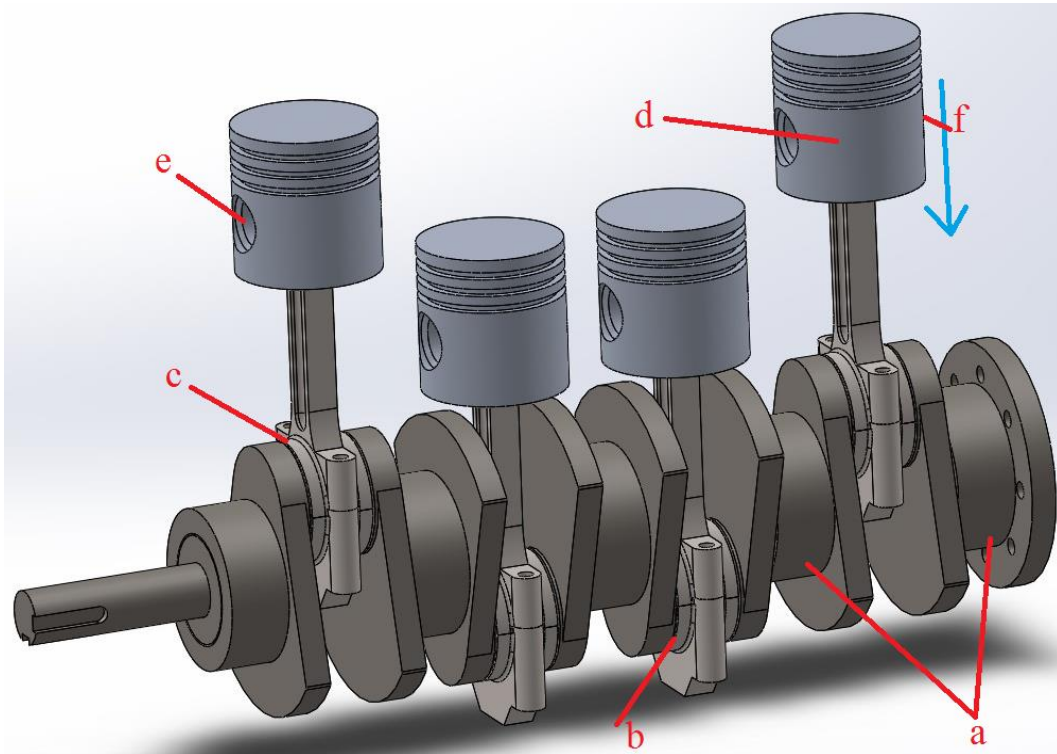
Dessin d'assemblage d'un moteur à combustion interne.
